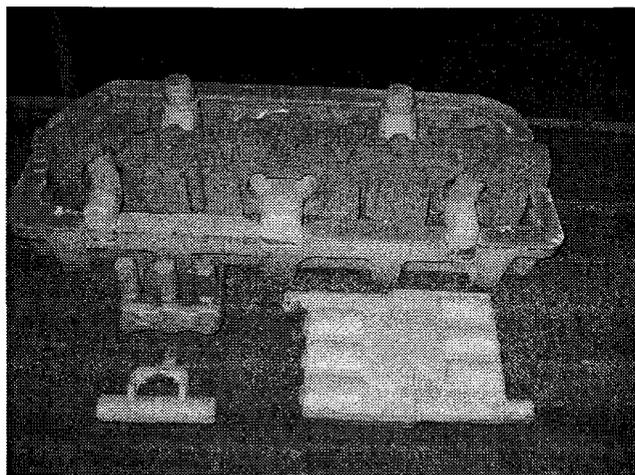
Стержень для отливки «Головка цилиндра», уложенный в стержневой ящик
